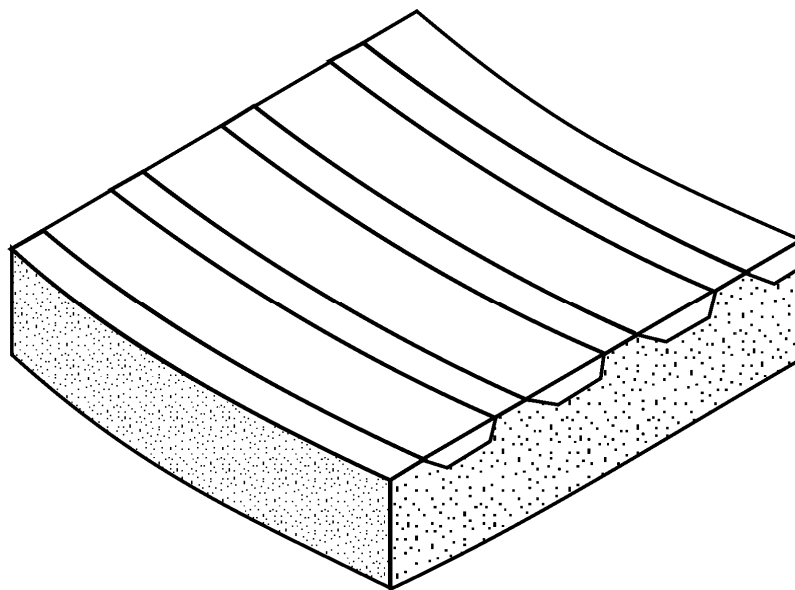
Підшипники канавкового типу фірми Міба
